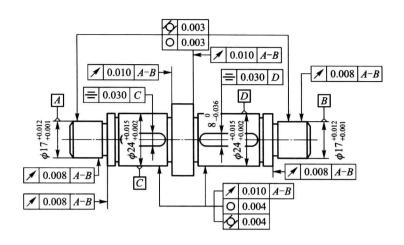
轴的几何公差标注示例 注: \$17 为与轴承配合直径,\$24 为与齿轮配合直径
